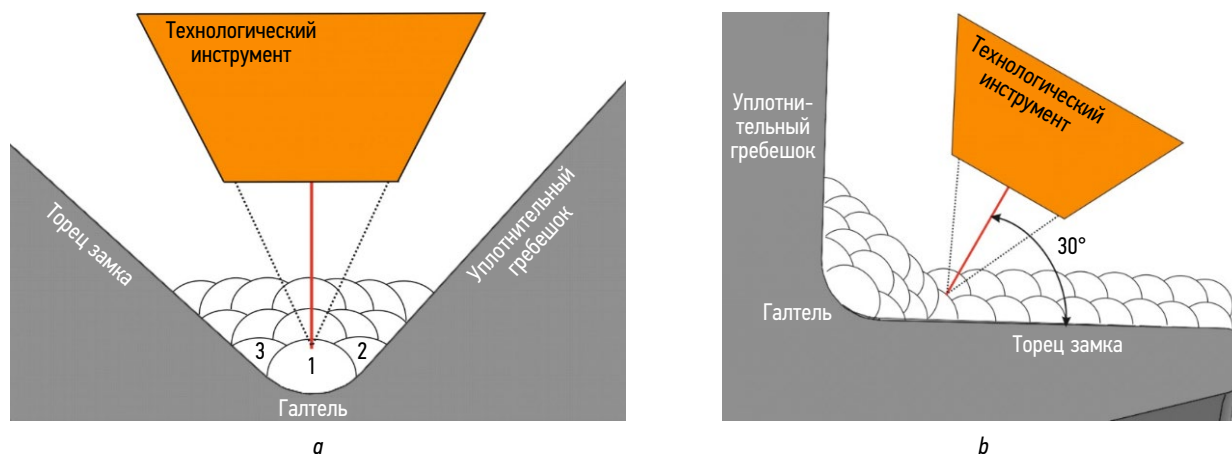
Схема наплавки изношенных поверхностей: *a* — схема наплавки галтели; *b* — схема наплавки торца замка.
